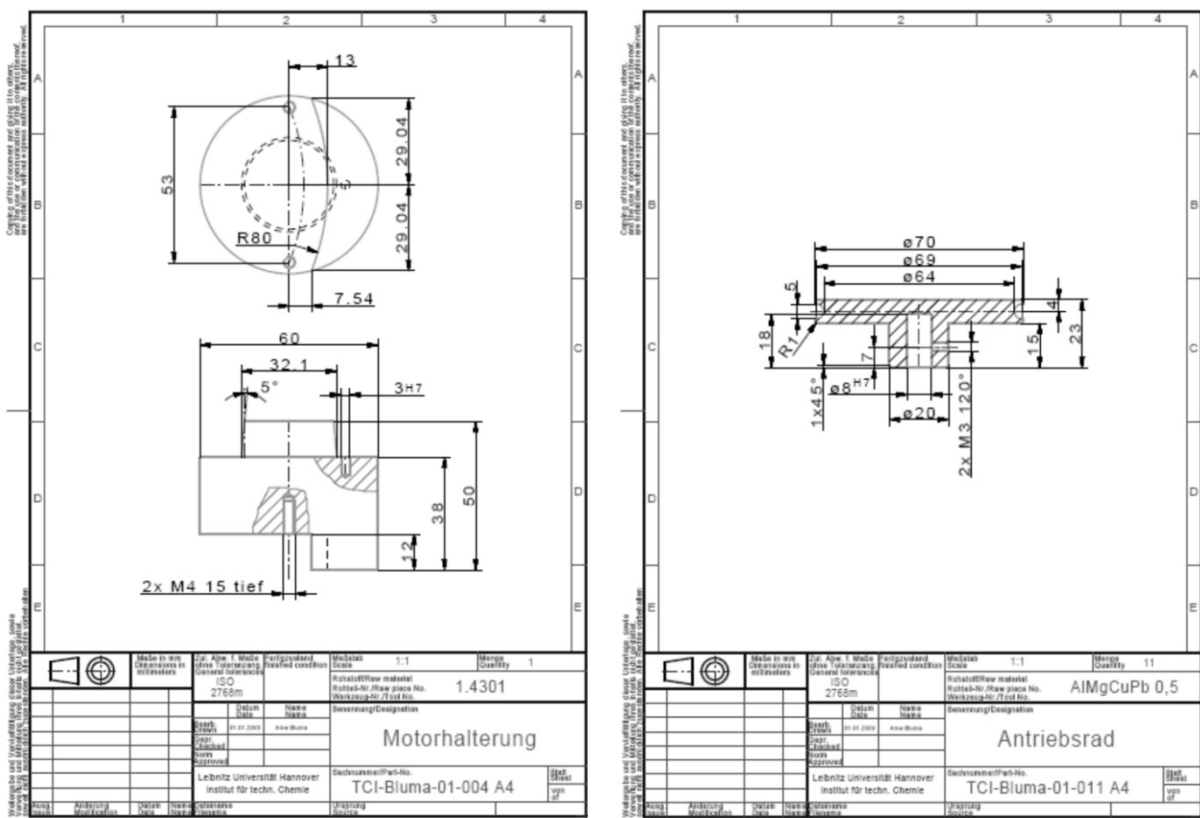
Technische Zeichnung der Motorhalterung (links) und des Antriebsrads (rechts).
